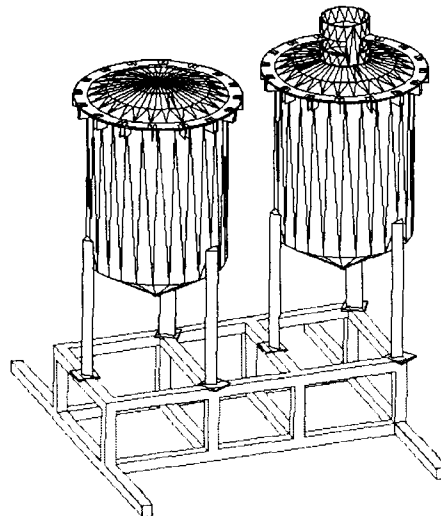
Soporte para tanques de sedimentación y lavado.
